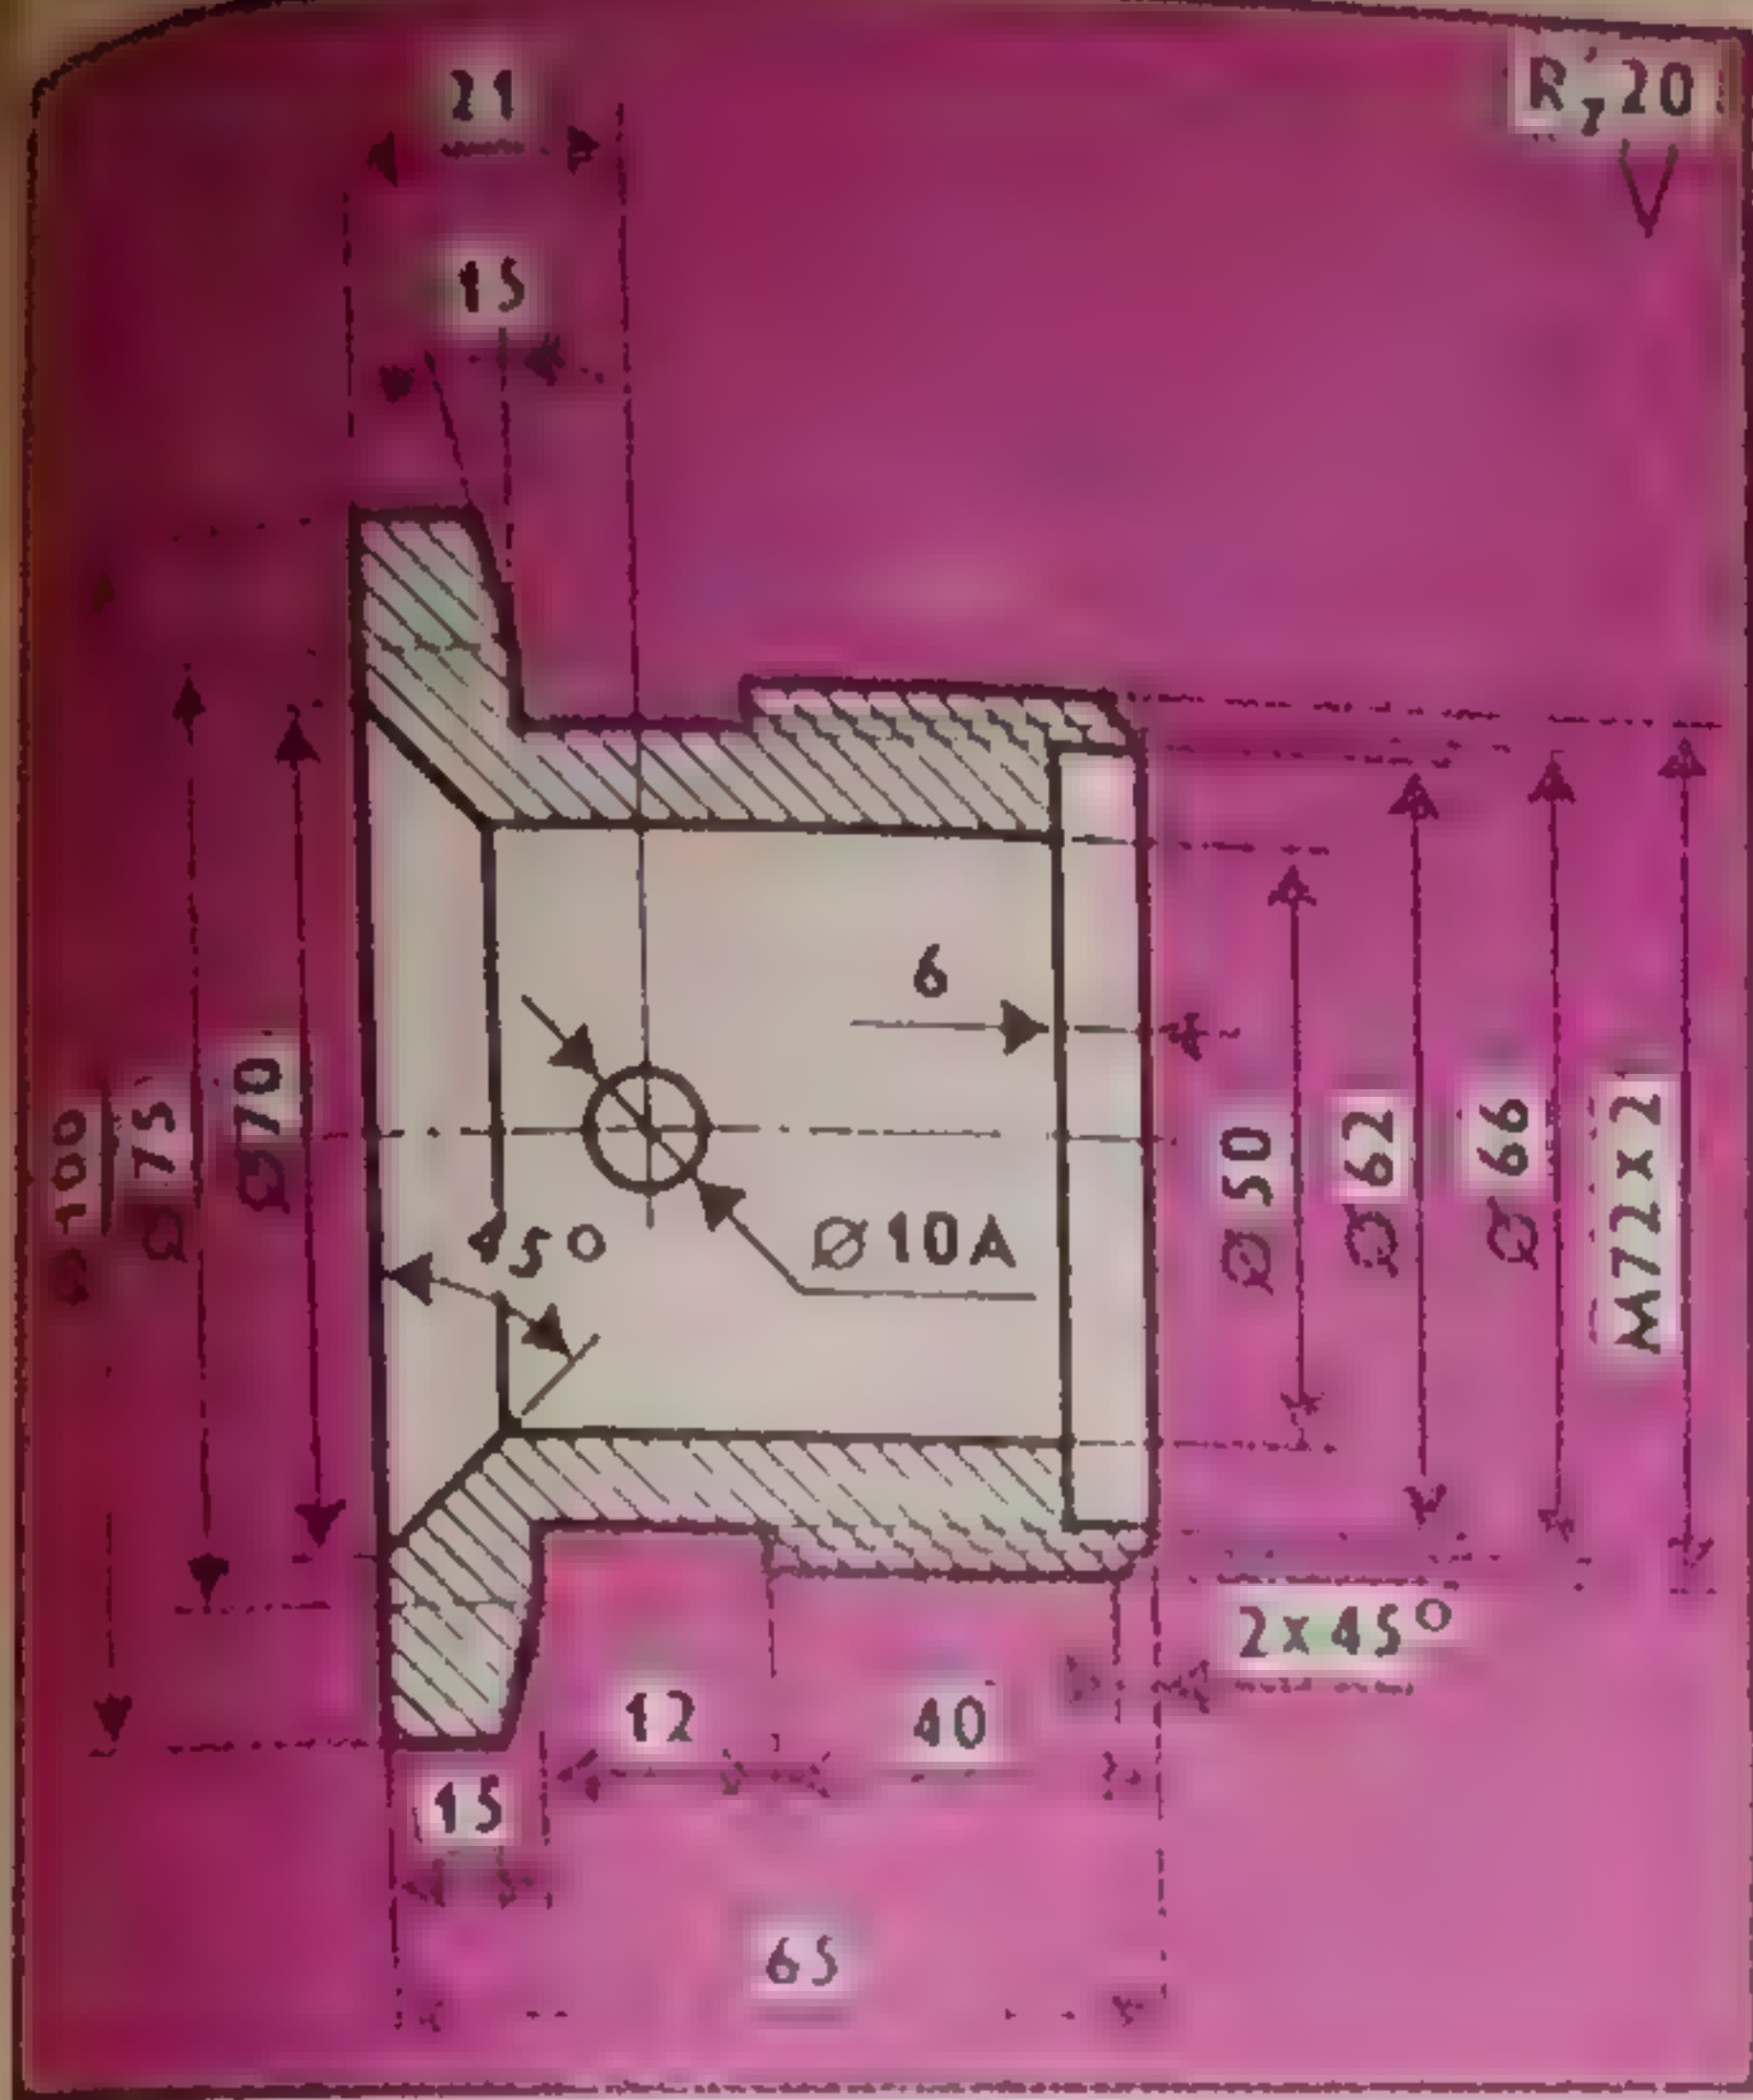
Гайка корпуса сальника фильтра, дет. 2—7
